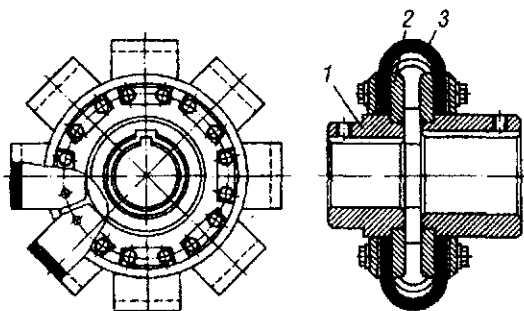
Схема муфты дробилки: 1 – втулка; 2 – диск; 3 – хомут
